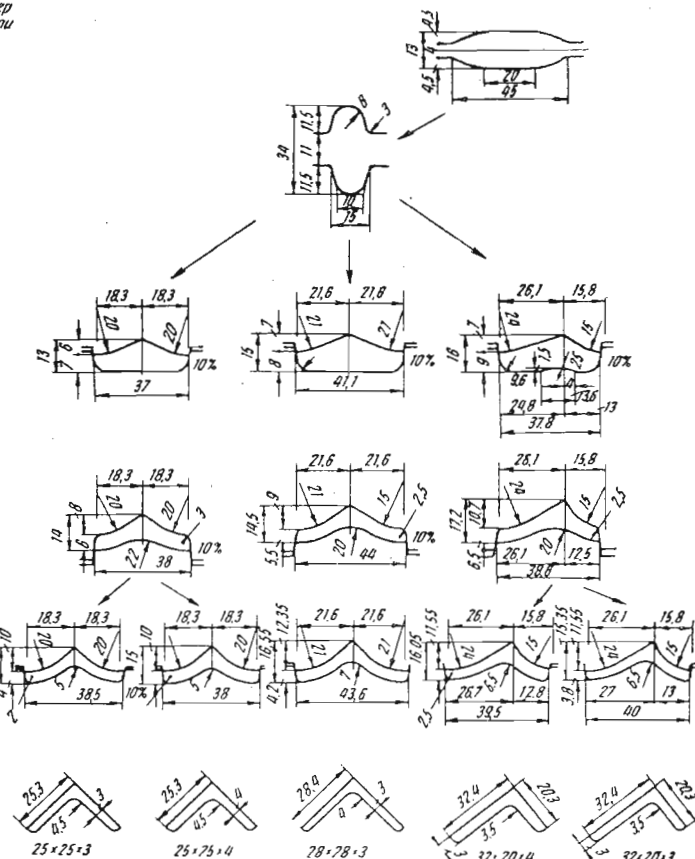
Калибровка угловой стали, прокатываемой на мелкосортном стане 250
